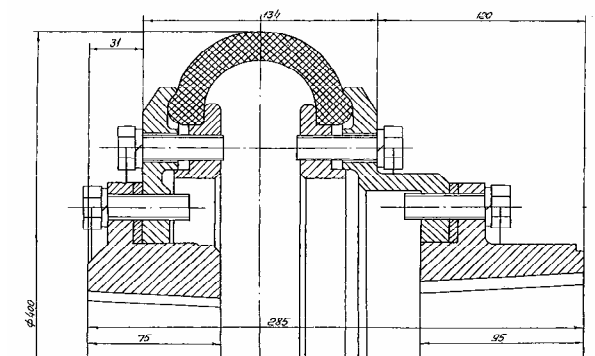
Муфта с резинокордной оболочкой 400×105 мотор-компрессора электровоза ВЛ10
